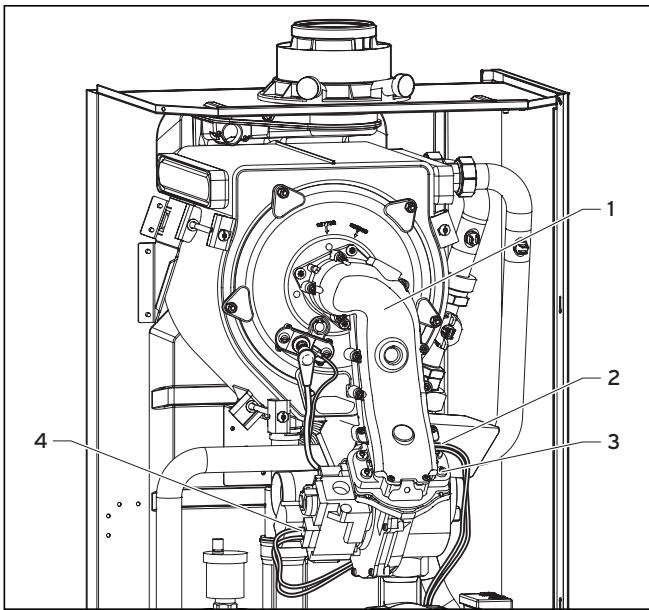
Демонтаж воздуходувки с газовой арматурой
